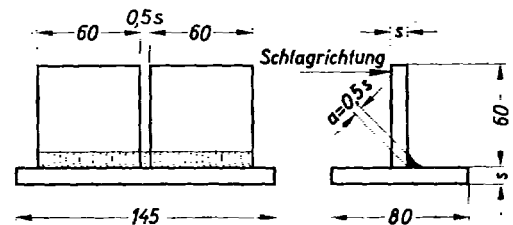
Winkelprüfstück für Blechschweißer an $s \geq 4$ mm
